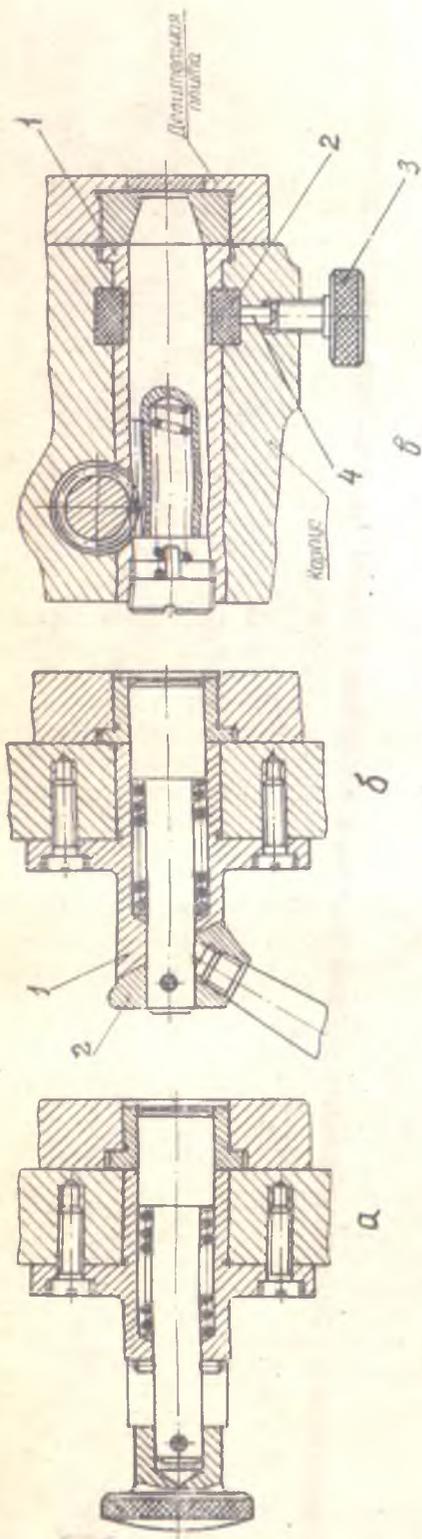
Конструкции фиксаторов: а, б — вытяжные, в — резьбый
